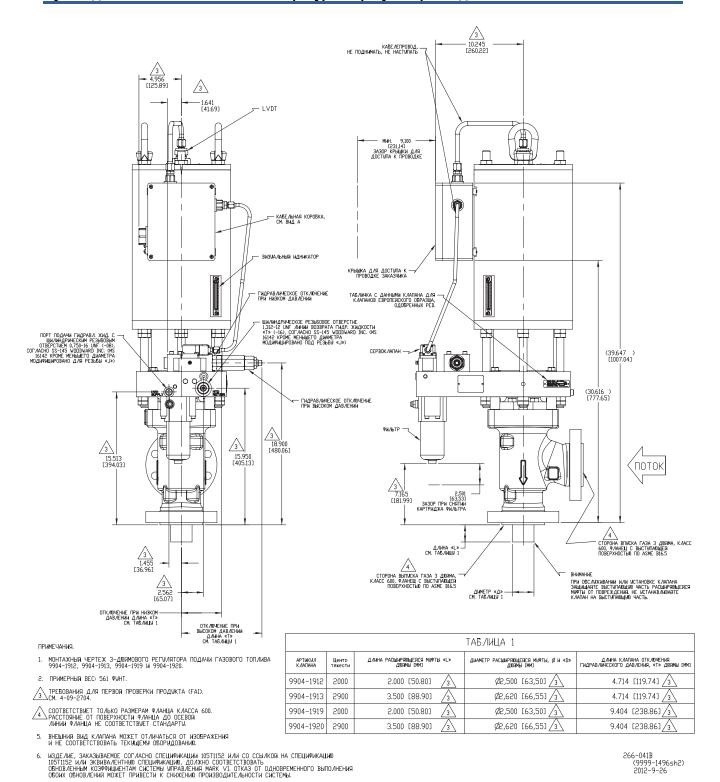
Габаритный чертеж регулятора SonicFlo (3 дюйма, класс 600)
